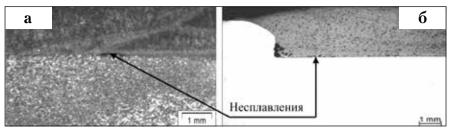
Несплавления на границе соединения основного и наплавленного металлов (4011) при плазменно-порошковой (a) и лазерно-порошковой наплавке (б) [6]
